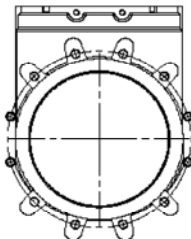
Конструкция ножевой шиберной задвижки Slide KGV-01/W
